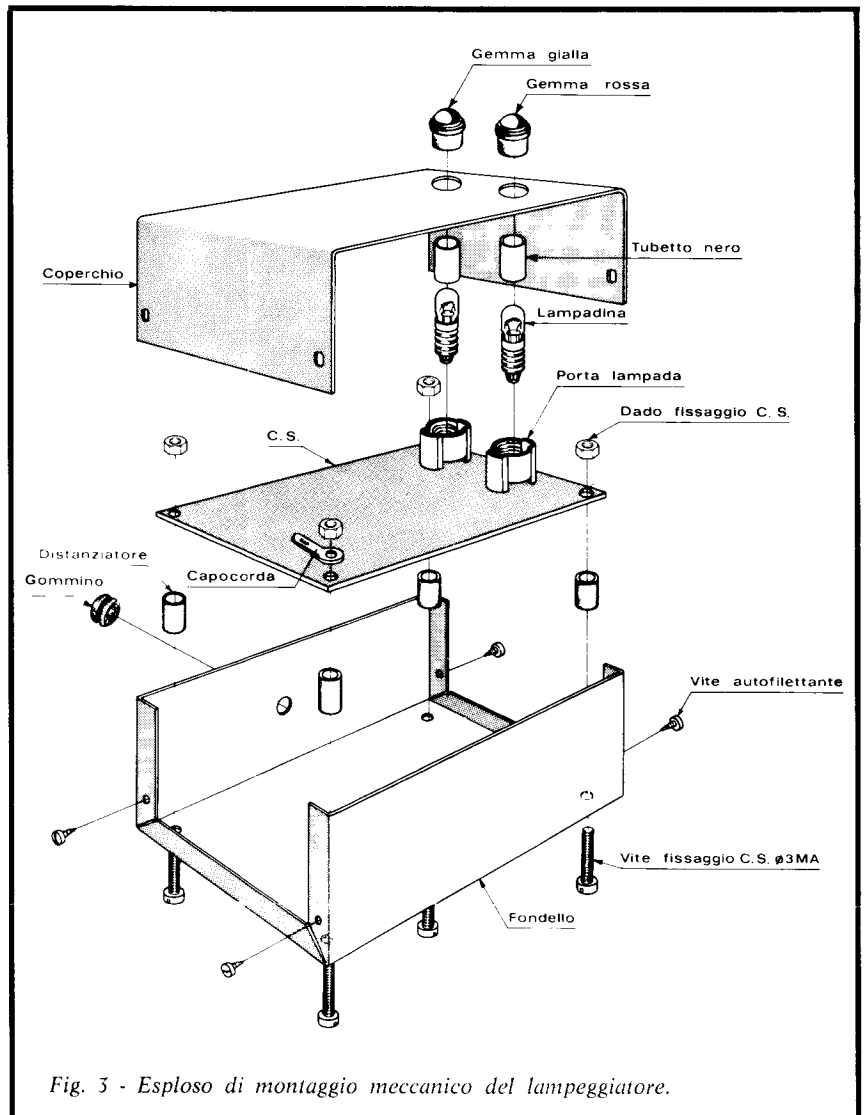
Esploso di montaggio meccanico del lampeggiatore.
